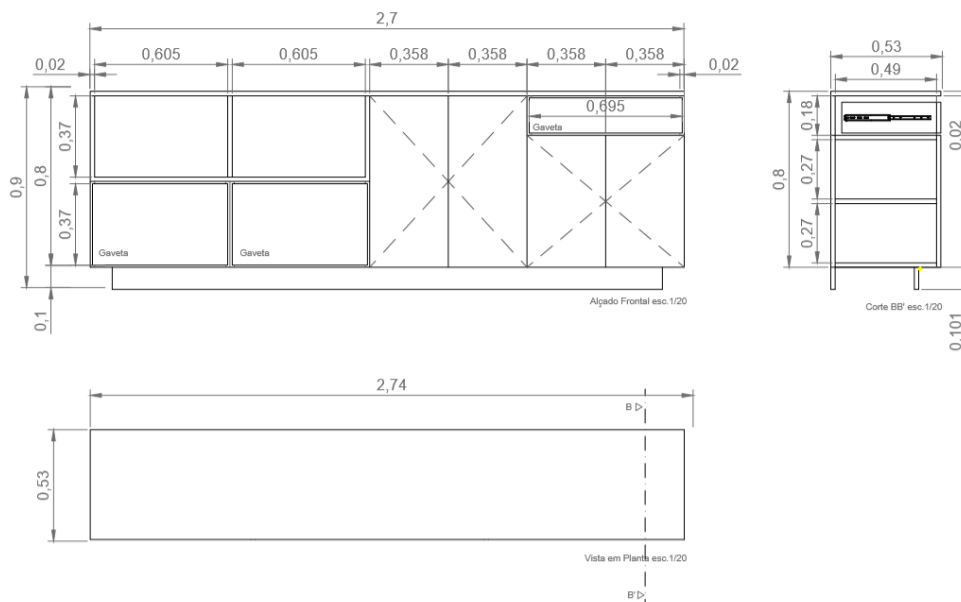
Desenho Técnico M02 - versão final. Escala 1/20. Fonte:autor
